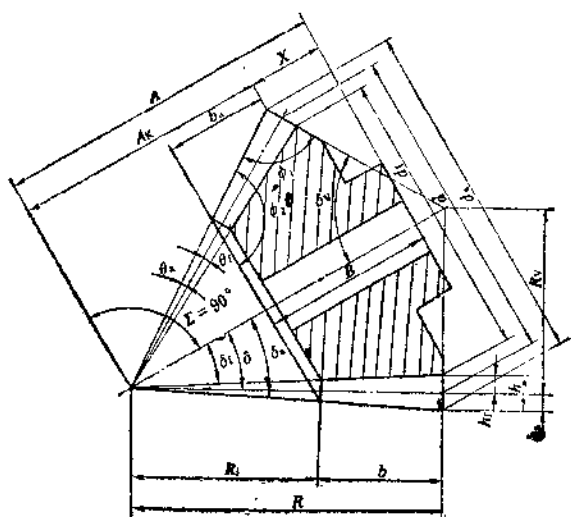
直齿锥齿轮传动几何要素（锥齿轮要素详图）
